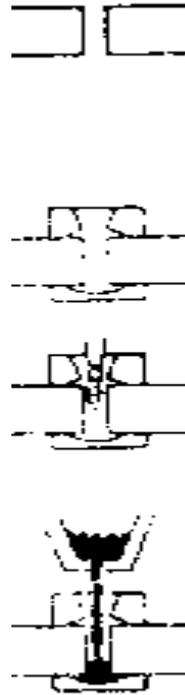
Equipamento básico para solda com Thermit®.
